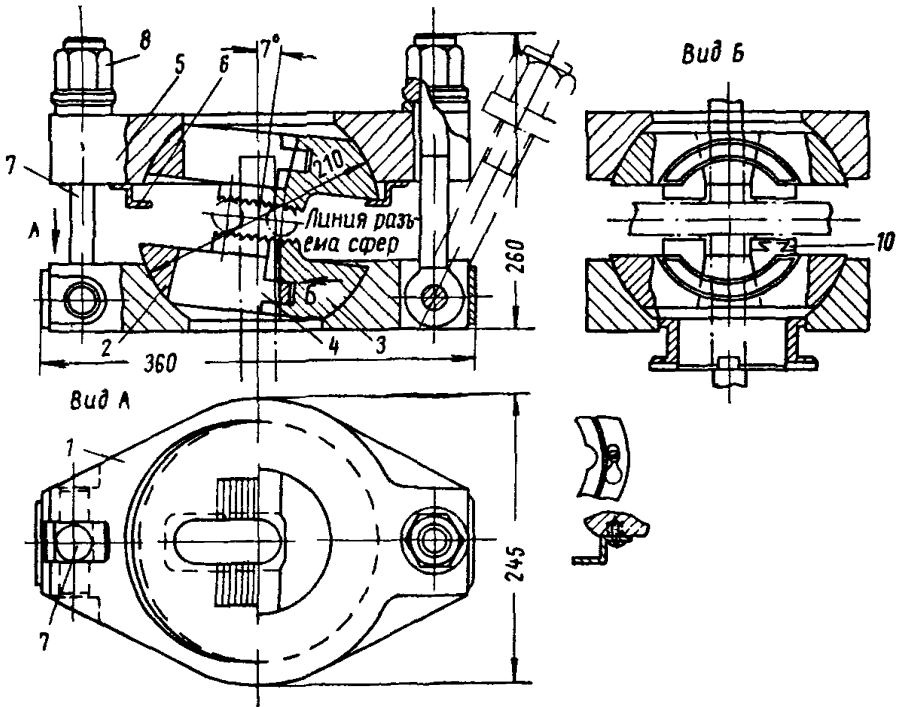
Приспособление для испытания на прочность образцов сварных крестообразных соединений трех стержней с помощью вертикальных разрывных машин
